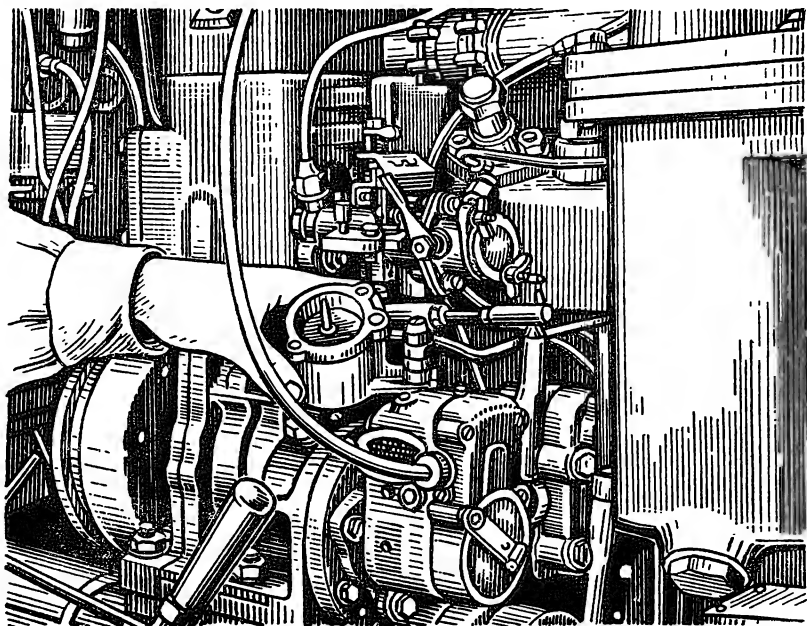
Снятие поплавковой камеры для промывки игельчатого клапана
